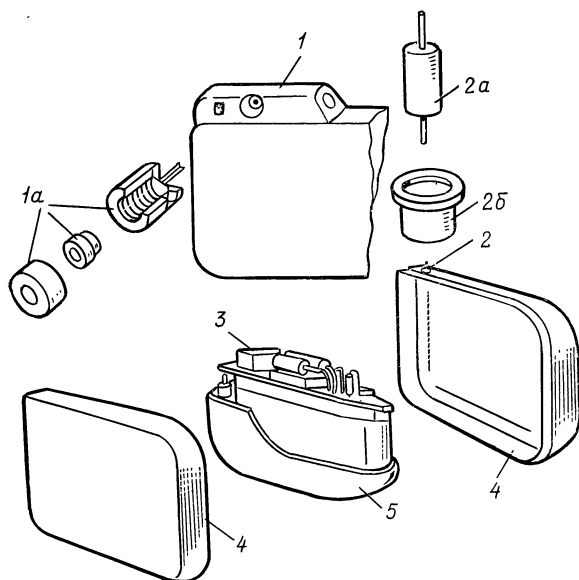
Основные элементы конструкции ЭКС II и III поколений: 1 — соединитель; 1а — детали соединителя; 2 — гермоввод; 2а — изолятор с проводом; 2б — кольцо гермоввода; 3 — электронная схема; 4 — корпус; 5 — источник питания
